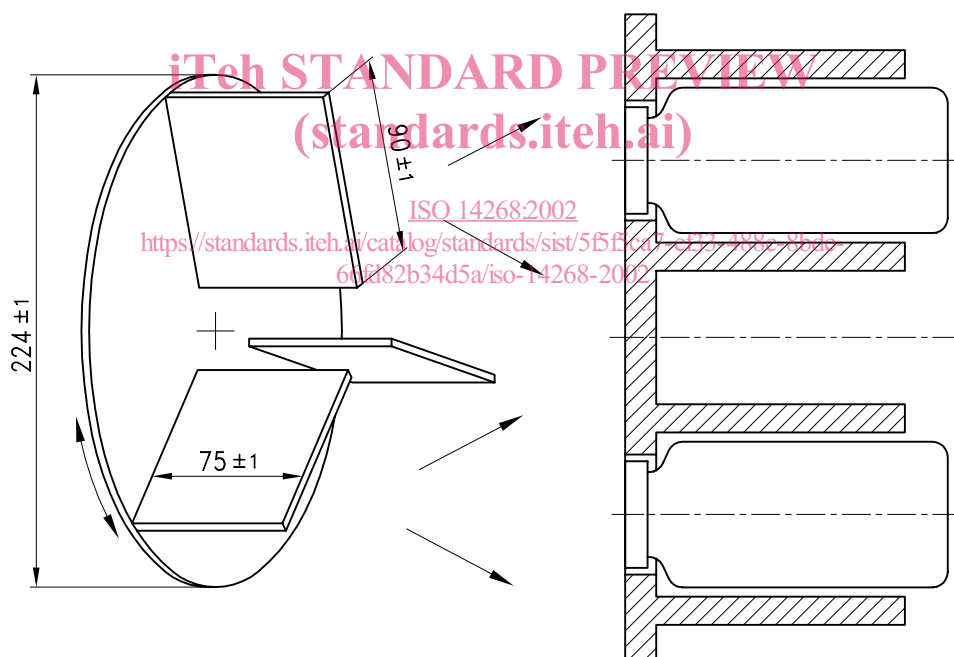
Configuration générale de la machine d'essai (toutes les dimensions en millimètres)
